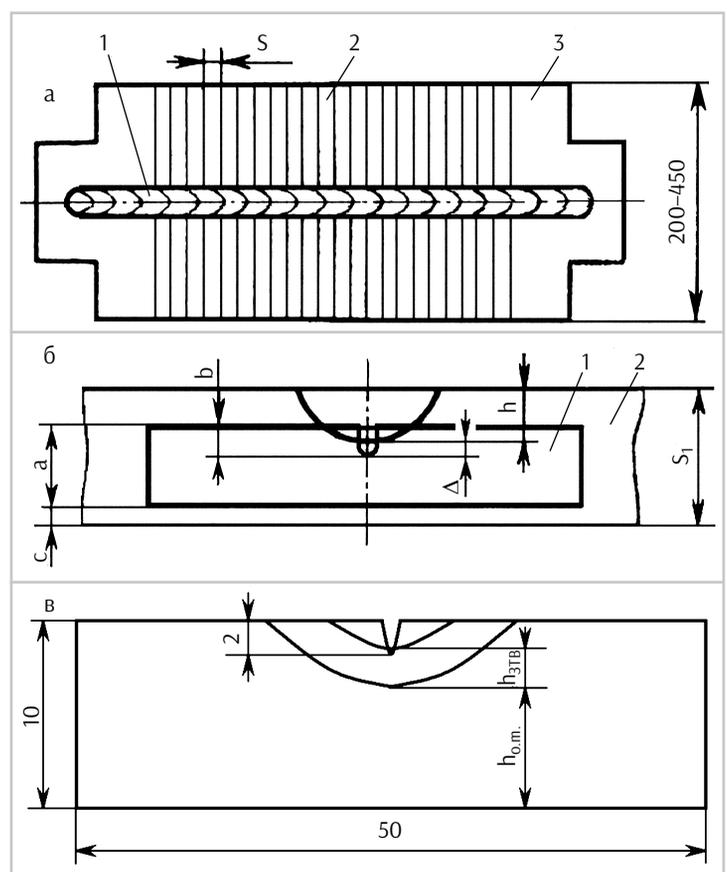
Валиковая проба с наплавкой (а), схема вырезки образцов для испытаний на ударный изгиб (б) и обозначение участков сварного соединения, которые входят в состав ударного образца (в): 1 — наплавленный валик; 2 — составные бруски; 3 — выводная планка; $h_{напл}$ — участок с наплавленным металлом; $h_{ЗТВ}$ — участок ЗТВ; $h_{о.м.}$ — участок основного металла.
